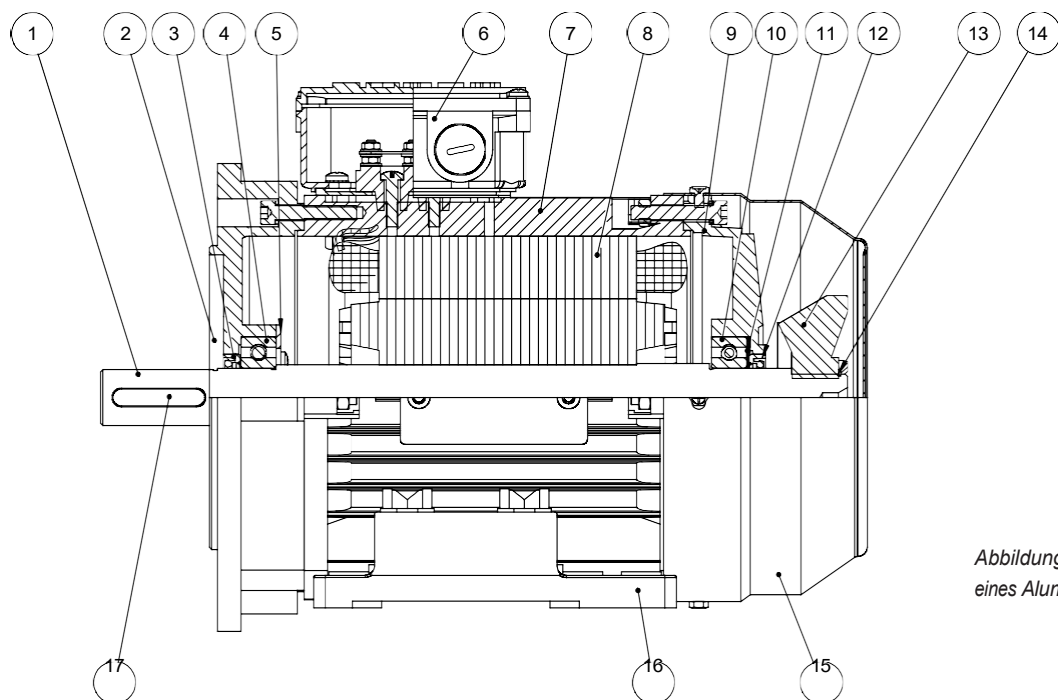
Querschnittsansicht eines Aluminiummotors
